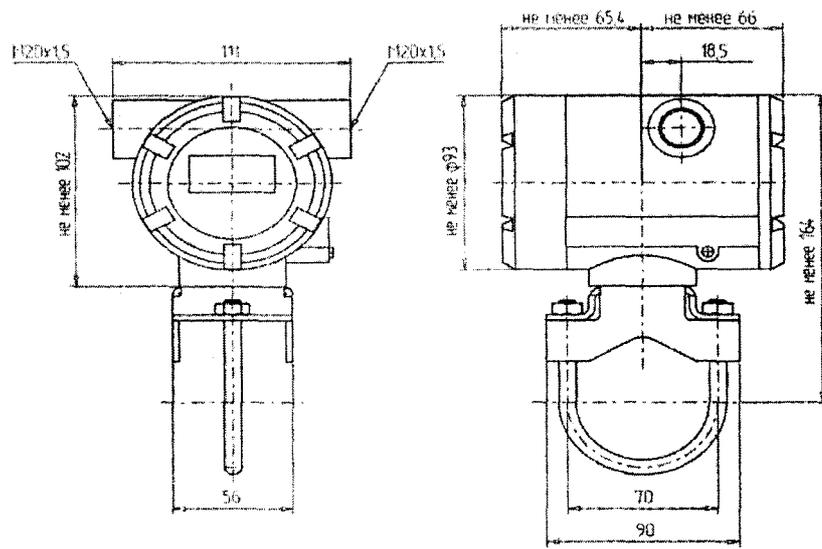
Преобразователь с HART протоколом в корпусе Д
